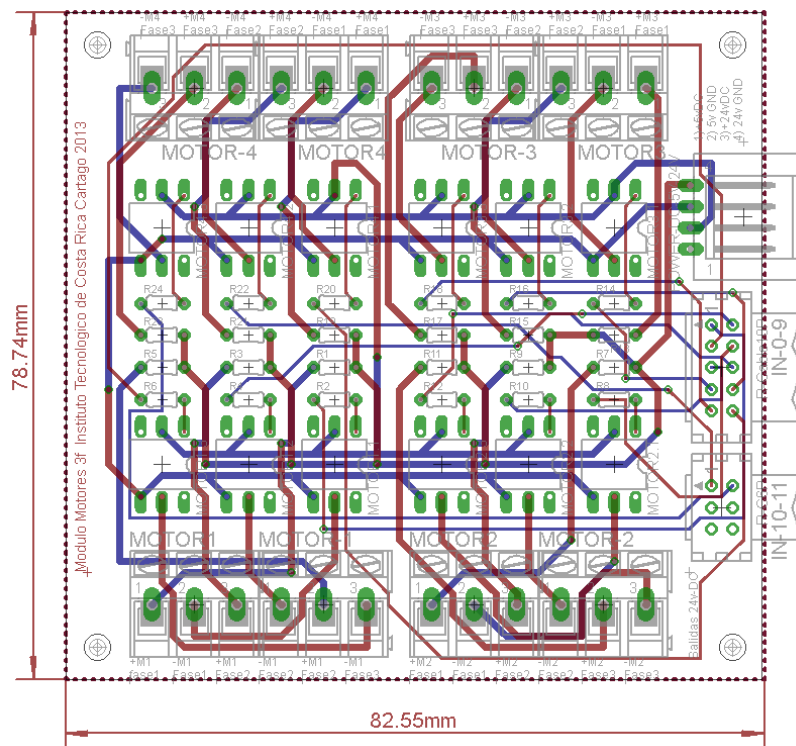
Circuito de control para motores trifásicos PCB completo
